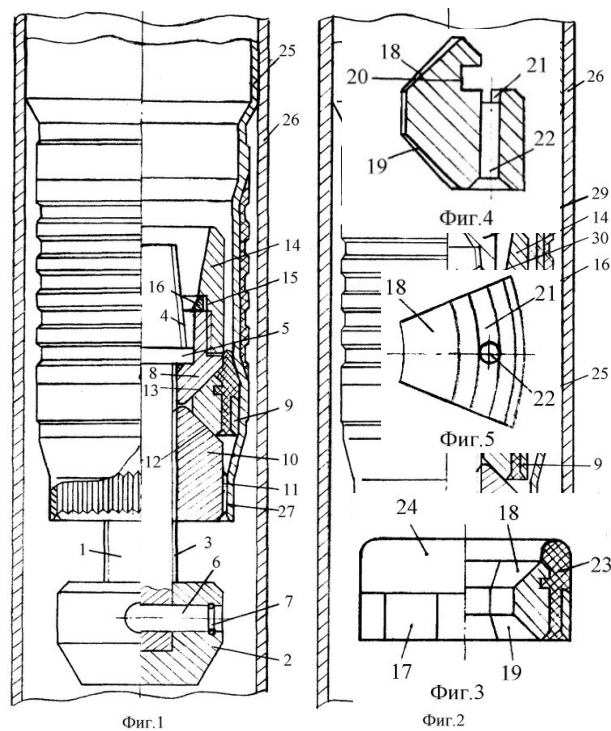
«Башмак для установки профильных перекрывателей в скважинах, где 1 – монтажный болт, 2 – съемная головка, 3 – левая резьба, 4 – правая коническая резьба, 5 – упорный бурт, 6 – штифт, 7 – стоп-кольцо, 8 – дополнительный упор, 9 – уплотнительный элемент, 10 – упорная гайка, 11 – насечка, 12 – коническая поверхность, 13 – коническую поверхность, 14 – конический растроб» [74], 15 – канавка, 16 – стопорное кольцо, 17 – сегменты, 18,19 – конические поверхности, 20,21 – проточки, 22 – отверстия, 23 – резина, 24 – кольцо, 25 – профильный перекрыватель, 26 – обсадная колонна, 27 – стенка суженного конца, 28 – развальцеватель, 29 – нижний конец, 30 – внутренняя коническая резьба, 31 – кольцевая проточка.
